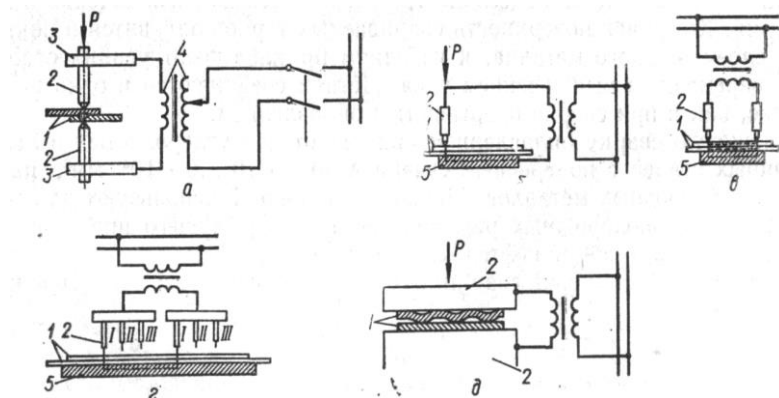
Основные схемы точечной контактной сварки
